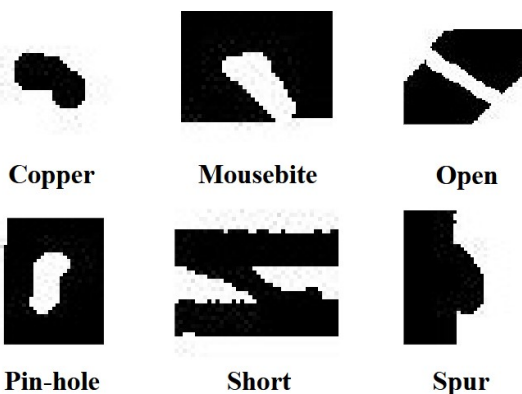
切割出來的 6 種 PCB 瑕疵區塊
